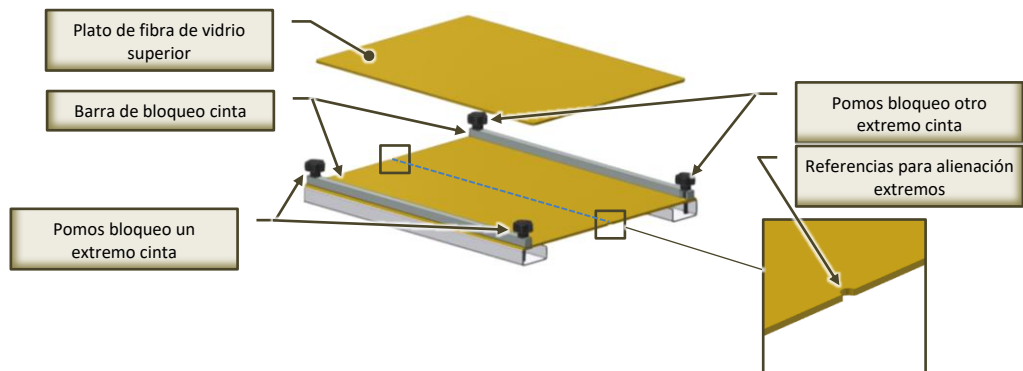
Posición cinta Fabric en placa de unión (partes)
